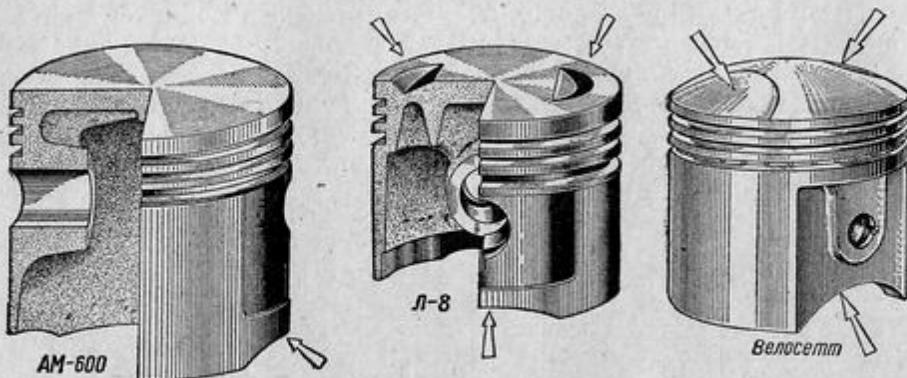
Поршни двигателей ТИЗ-АМ-600, Л-8 и Велосетт.
